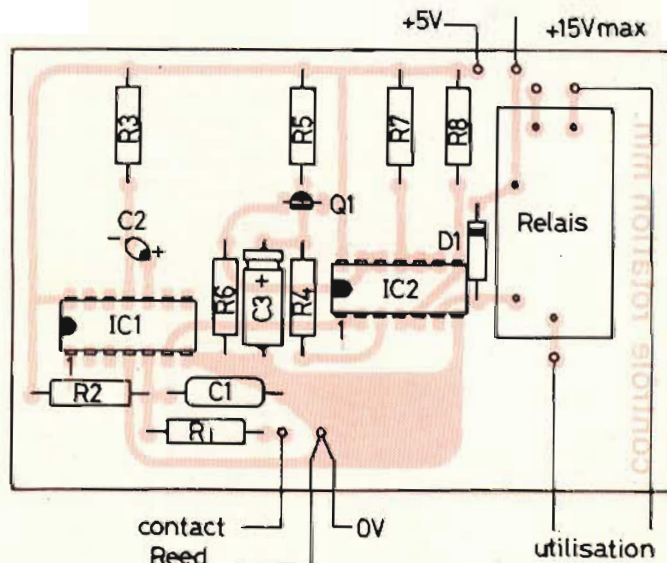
Il circuito stampato di cui alla figura 4, visto dal lato componenti.
